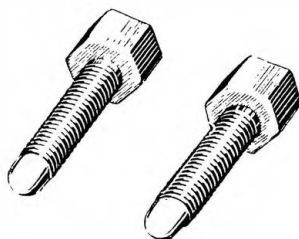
Два болта 47001-1-064П для снятия опорного диска дет. 237-10-8 главного фрикциона
